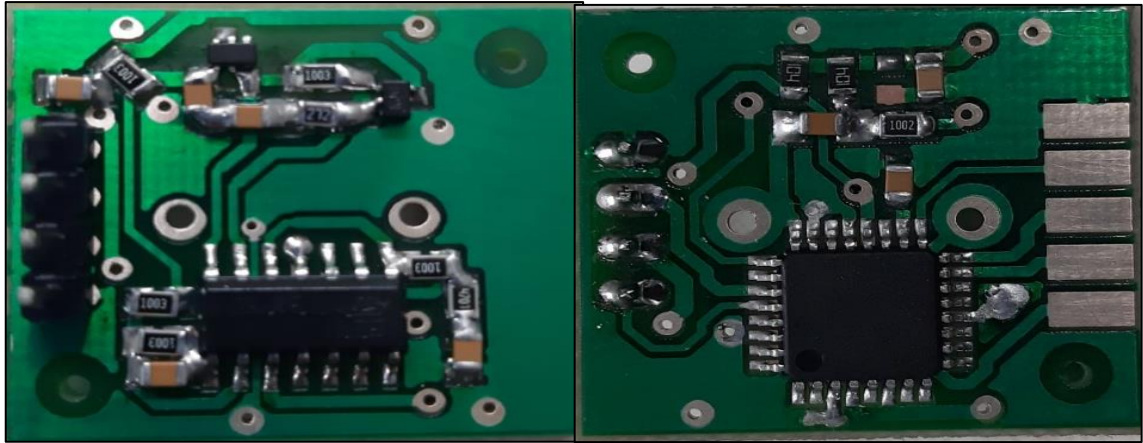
Implementación de PCB optimizada del sensor JA-002
